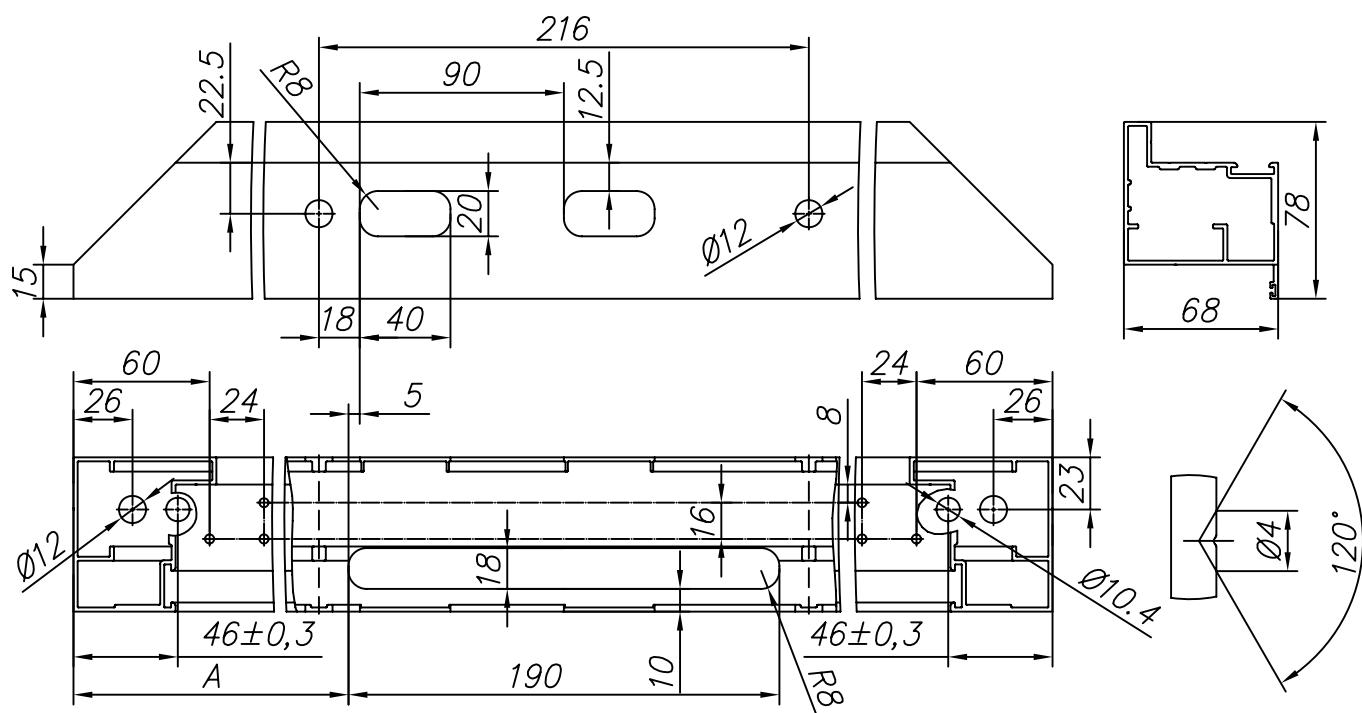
Изготовление стойки без паза для замка из профиля FLGU.400.0110 (открывание внутрь)
